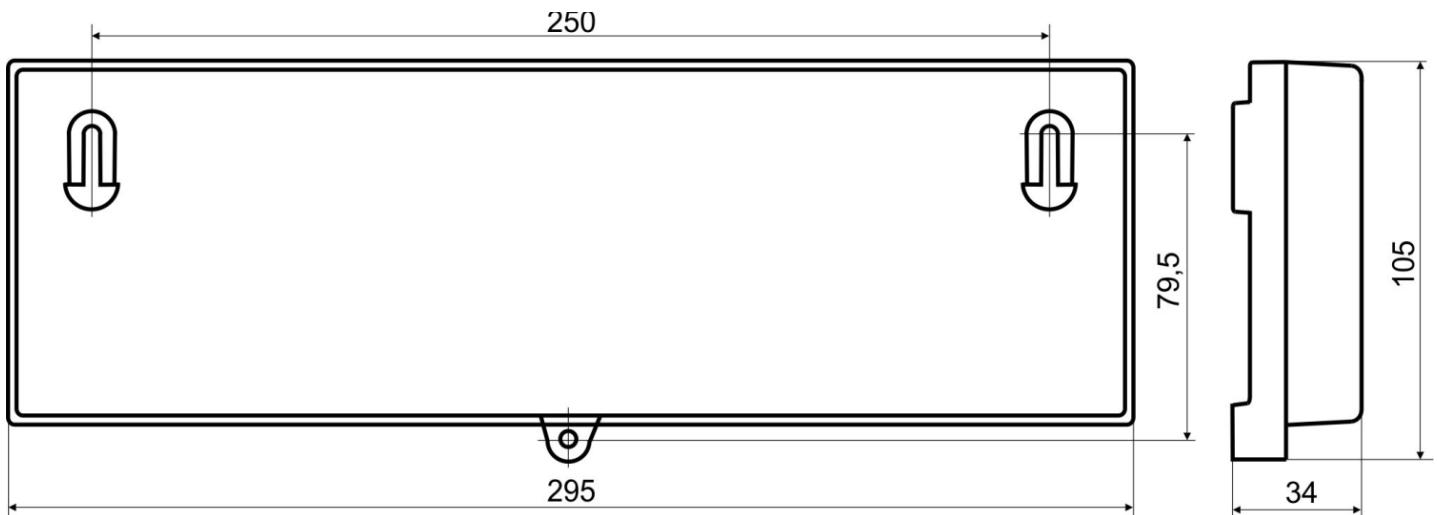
Габаритные и установочные размеры блока клавиатуры
